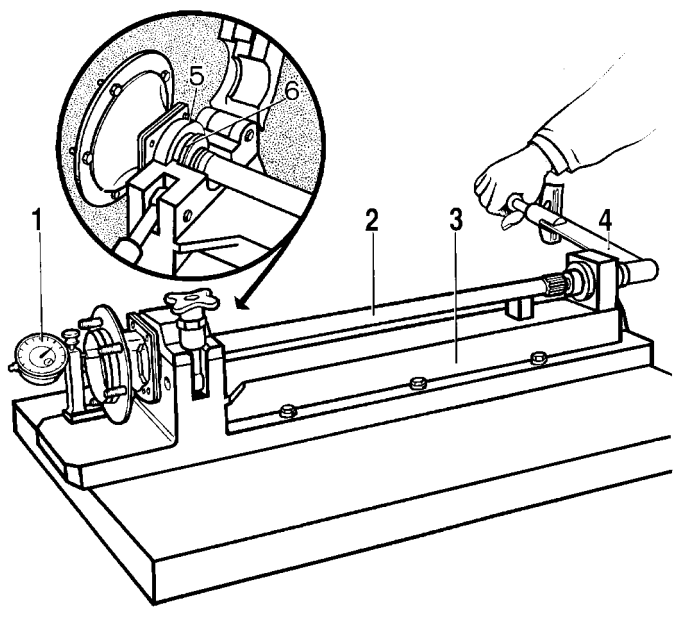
Запрессовка подшипника и запорного кольца подшипника полуоси:
